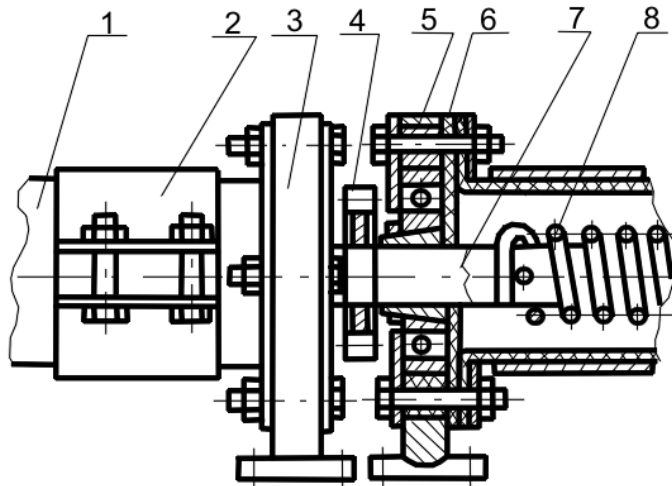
Схема привода спиральной цепью: 1 – труба; 2 – патрубок подвода удобрения; 3 – корпус подшипника; 4 – звездочка привода спиралей; 5 – уплотнение; 6 – уплотнение от слива жидкости; 7 – вал; 8 – спираль
